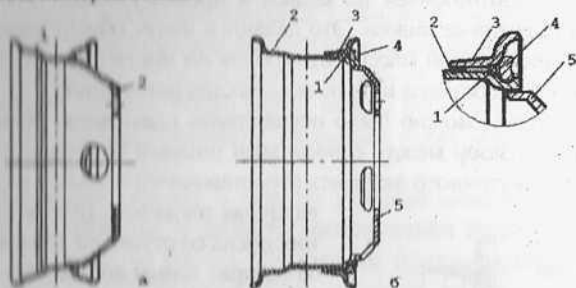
Конструкция колес для бескамерных шин: а – глубокий неразборный обод колеса; 1 – обод; 2 – диск; б – разборный обод колеса 8,50-21, предназначенного для автомобилей МАЗ: 1 – резиновый уплотнитель; 2 – обод; 3 – бортовое кольцо; 4 – замочное кольцо; 5 – диск
